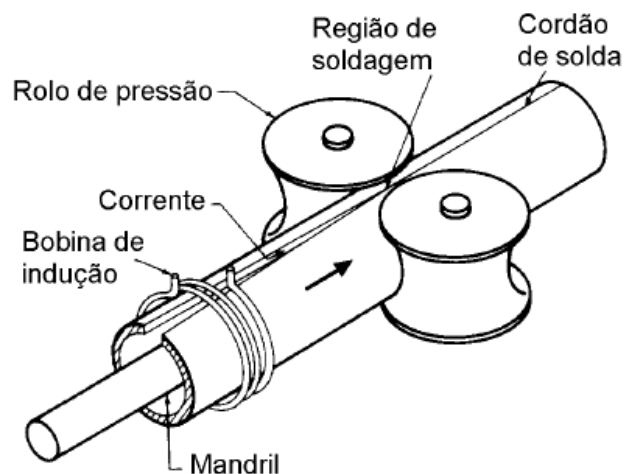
Processo de fabricação de tubo de aço com a utilização de soldagem por alta frequência (MARQUES et al, 2005).
